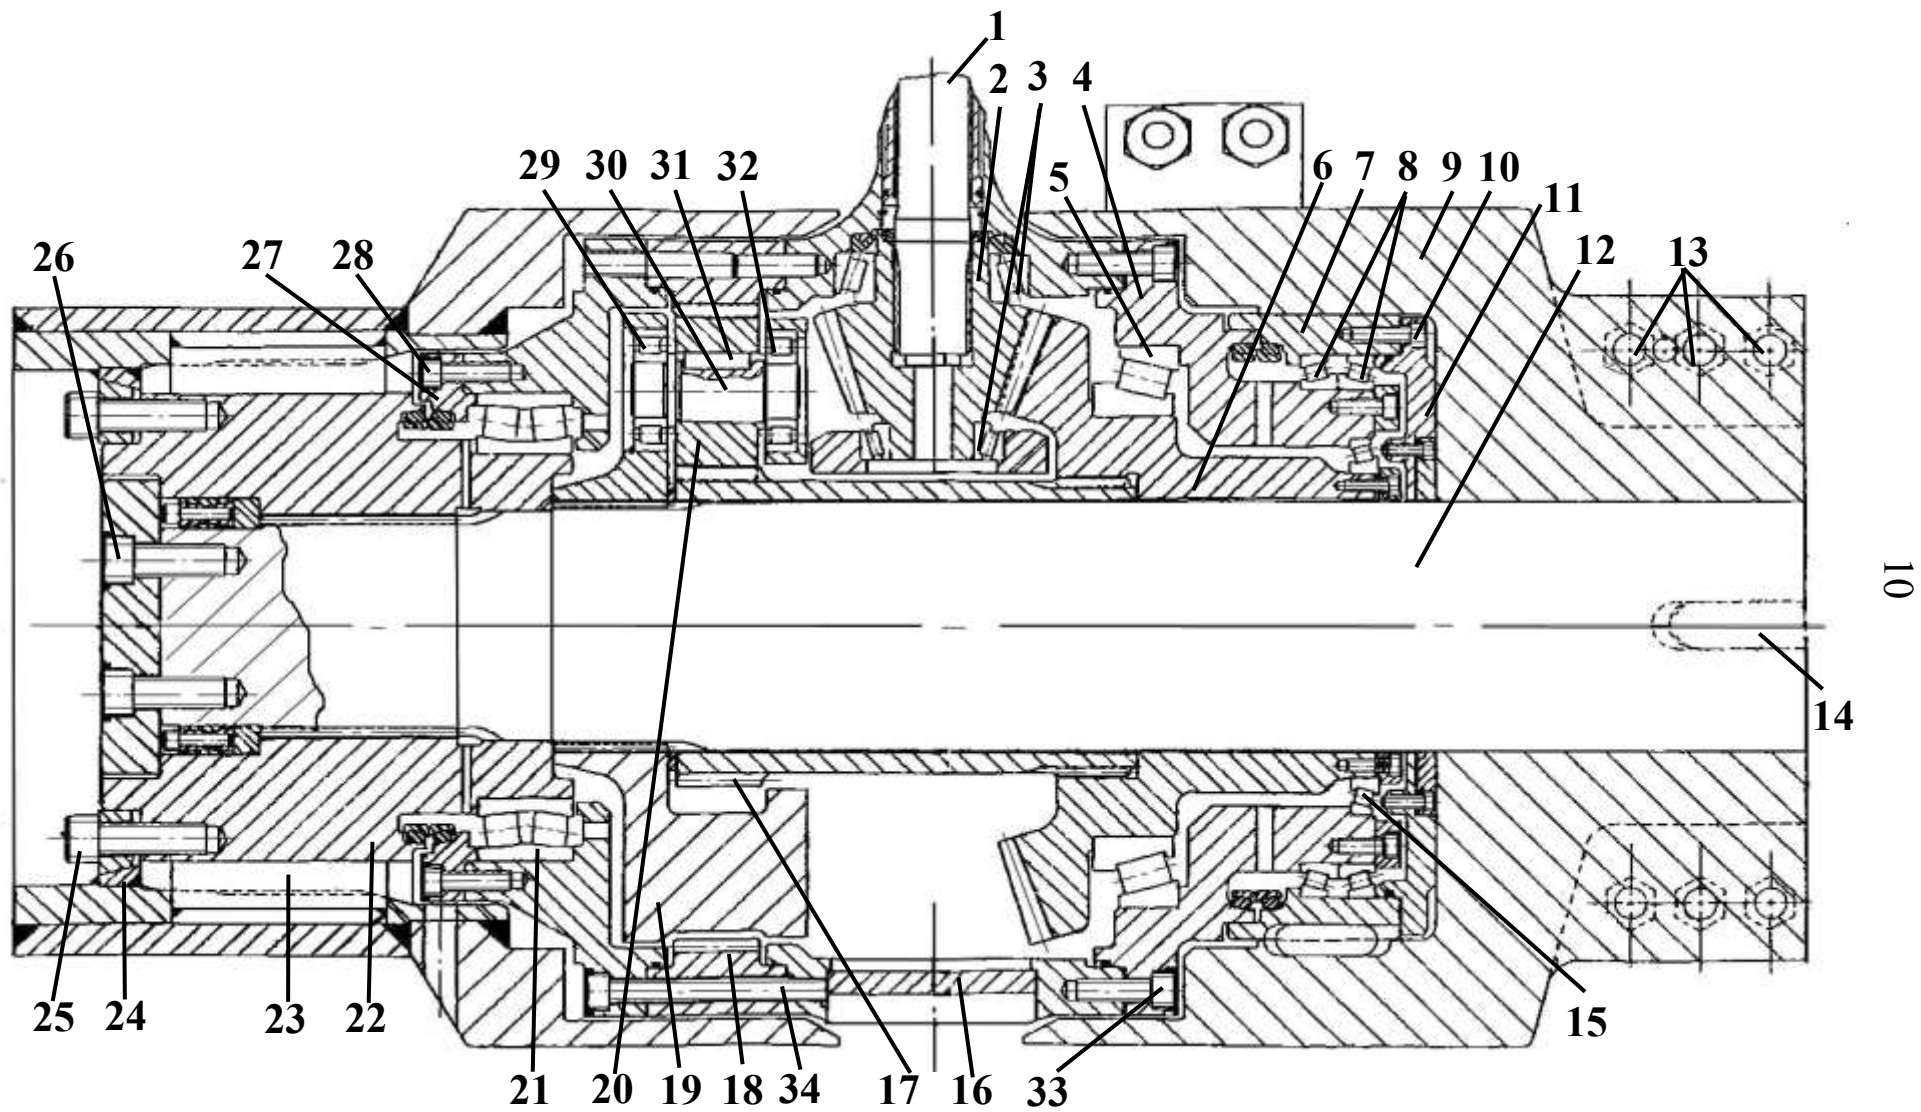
Конструкция правого редуктора барабана врубового агрегата комбайна 12СМ15
